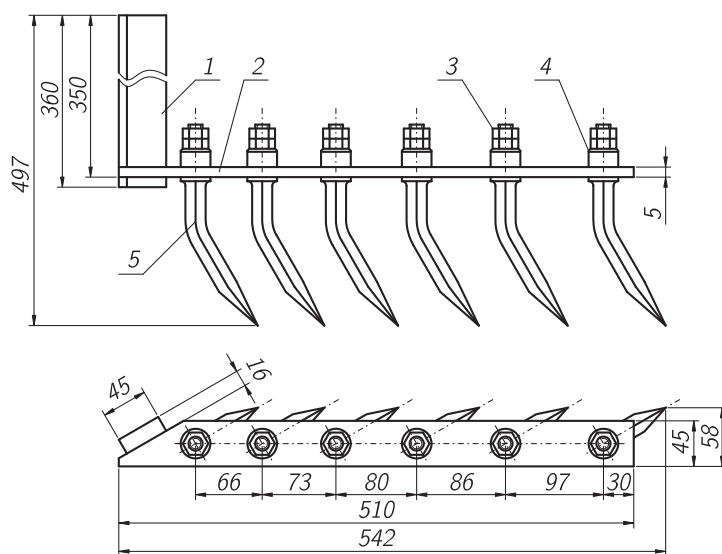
Предлагаемый зубчатый загортач (окончательный вариант):
